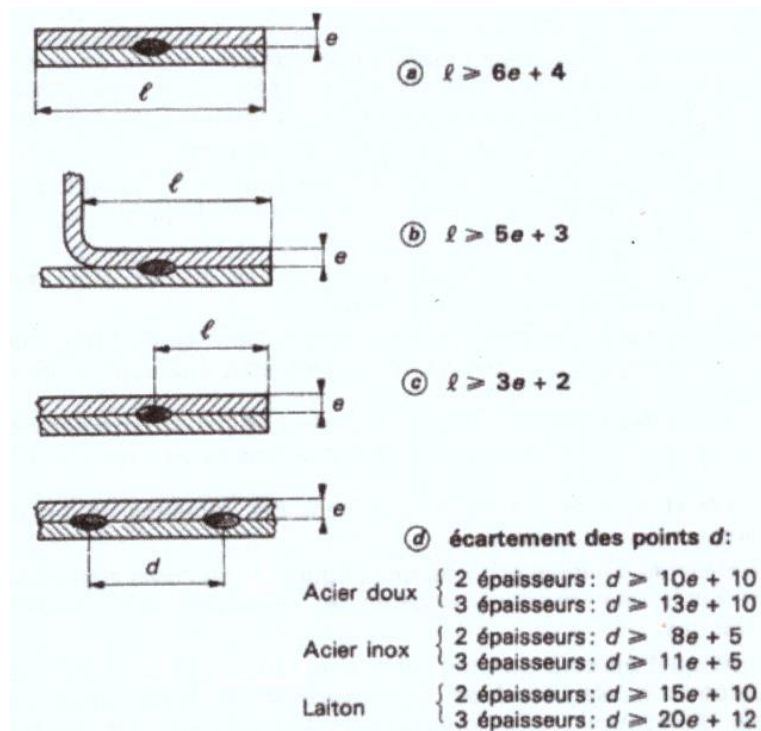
Soudage par points : position des points de soudure (dimensions au mm)
